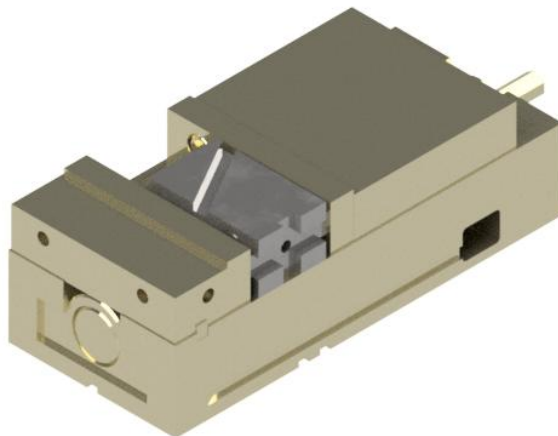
Пристосування для фрезерування супорта для встановлення картриджа
